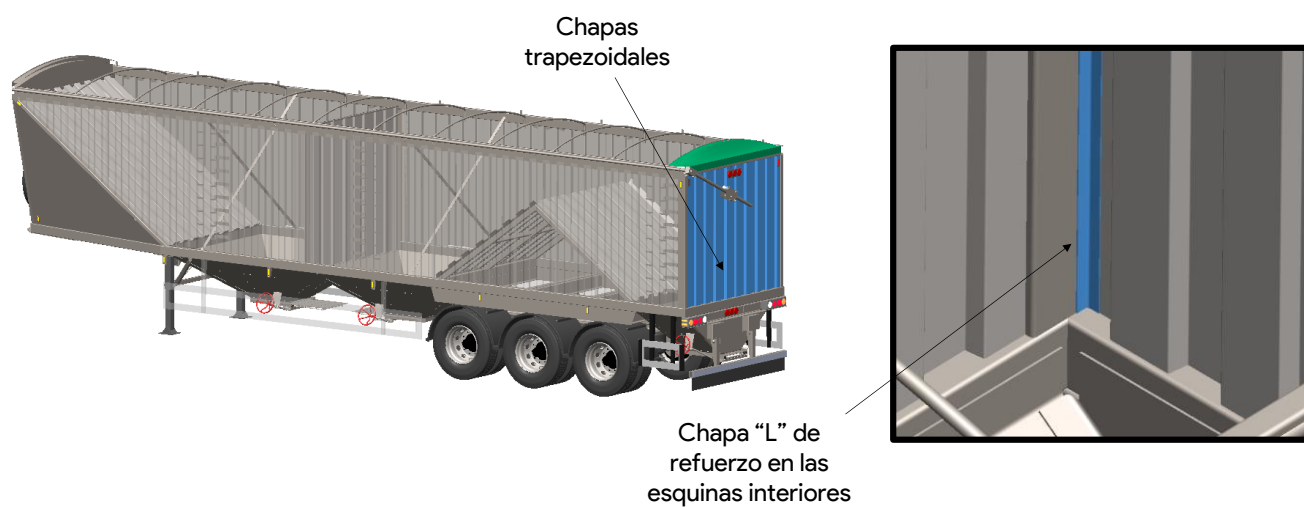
Chapas trapezoidales traseras y detalle de chapa "L" de refuerzo en el interior.
